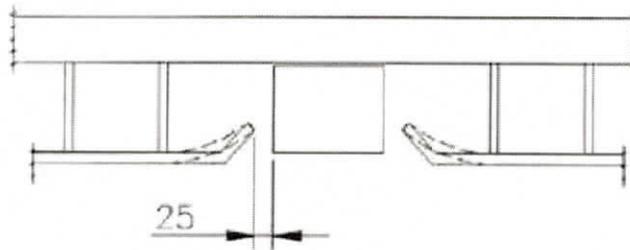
, Holgura con componentes del vehículo, Vista Superior (dimensiones en mm)
